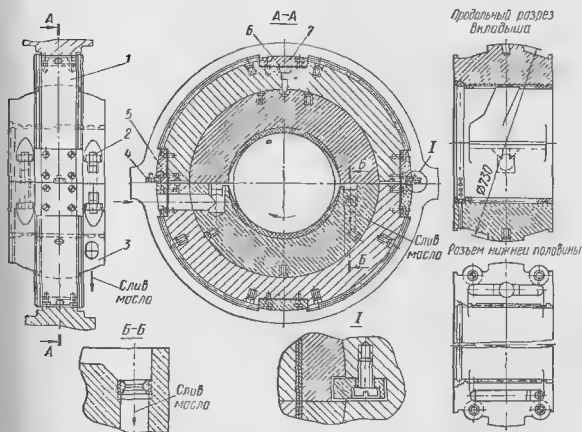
Самоустанавливающийся вкладыш опорных подшипников турбин ХТГЗ
